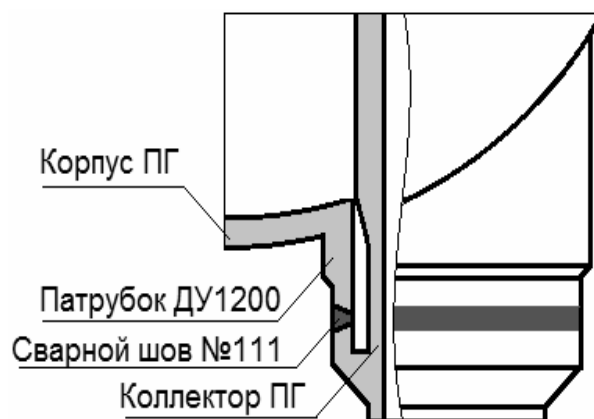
Сварное соединение №111 и его расположение в парогенераторе
